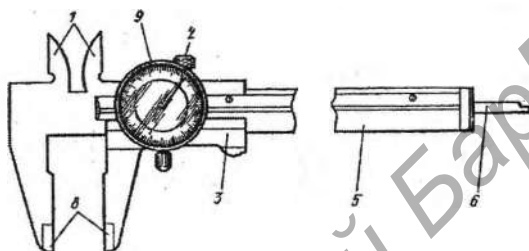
Штангенциркуль ШЦ-III (модель со стрелочной индикацией): 1 — губки для внутренних измерений, 2 — зажим, 3 — рамка, 5 — штанга, 6 — линейка глубиномера, 7 — нониус, 8 — губки для наружных измерений, 9 — отсчетное устройство [10, с. 153]
